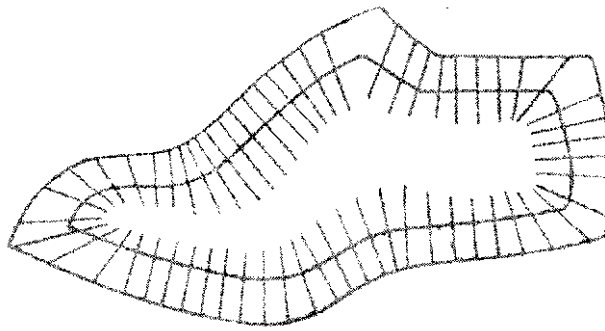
Одержання розгортки бокової поверхні колодки
